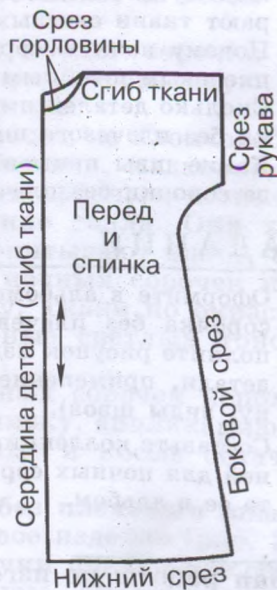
Названия детали и срезов выкройки ночной сорочки без плечевого шва
